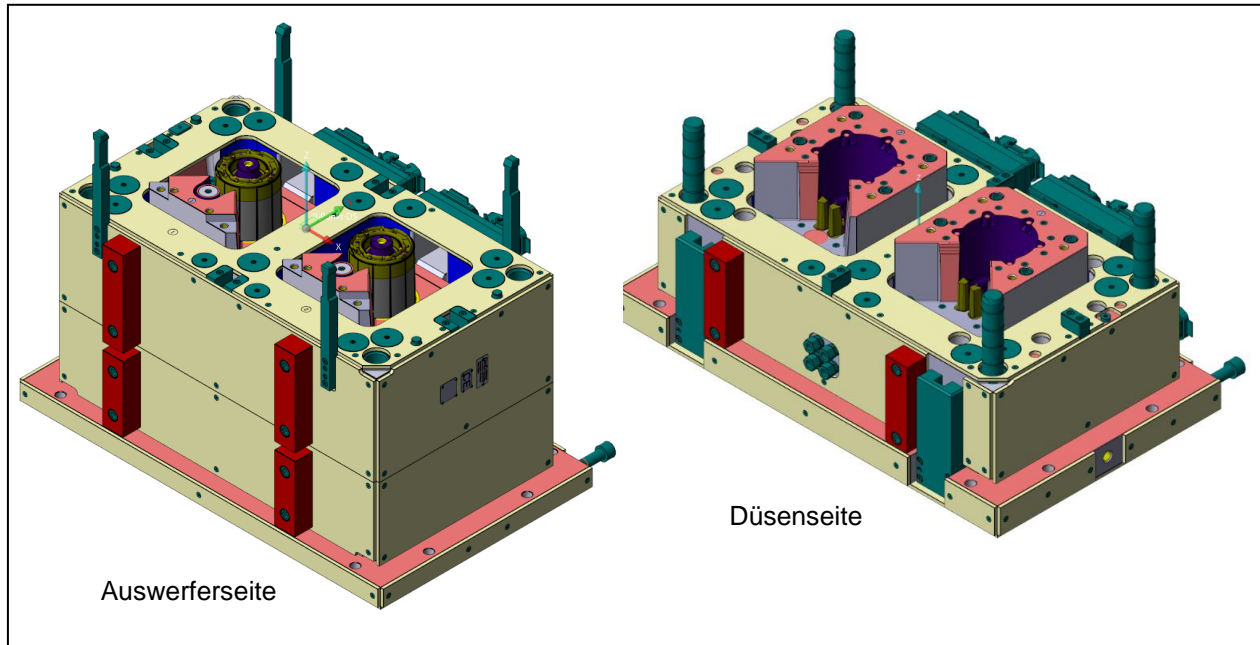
Demonstrator-Werkzeug Elektromotorgehäuse 2-fach (Quelle: GHD)
